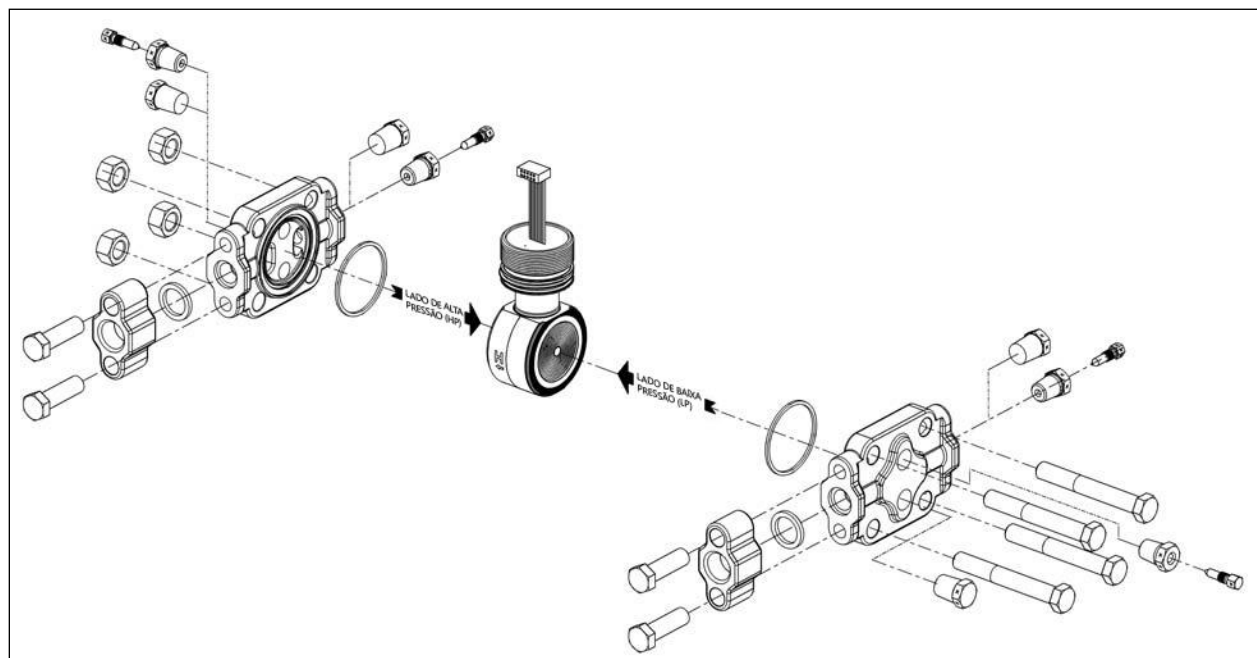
Corpo de transmissor STG730, 740, 770 e STA722, 740 (Ref.)
